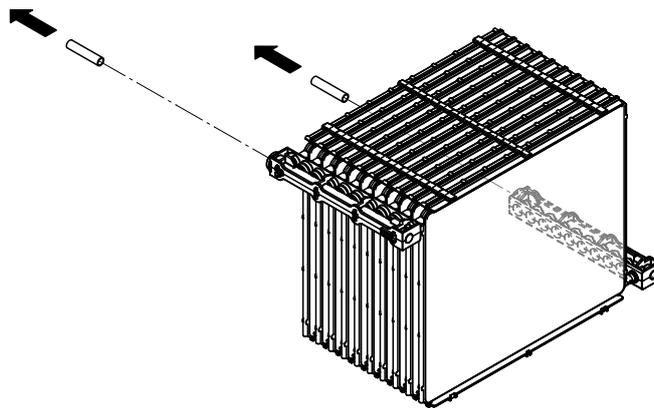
Schlauchstücke entfernen und Anschlüsse verschliessen
